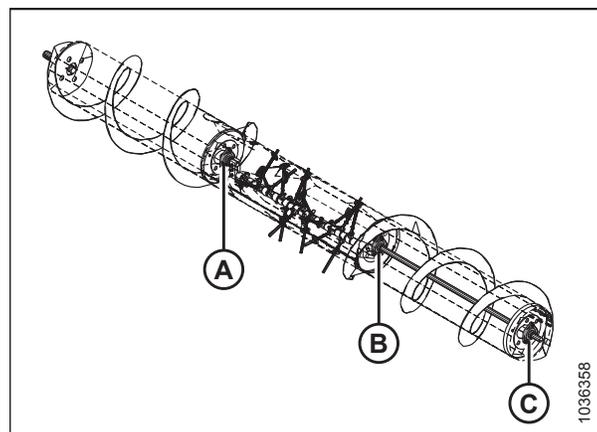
Rodamientos con accesorios de engrase en el sinfín: vista desde el lado derecho
